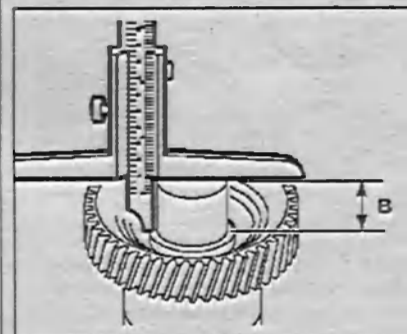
Измерьте размер «В» от верхнего края промежуточного вала до манжеты седла подшипника.
